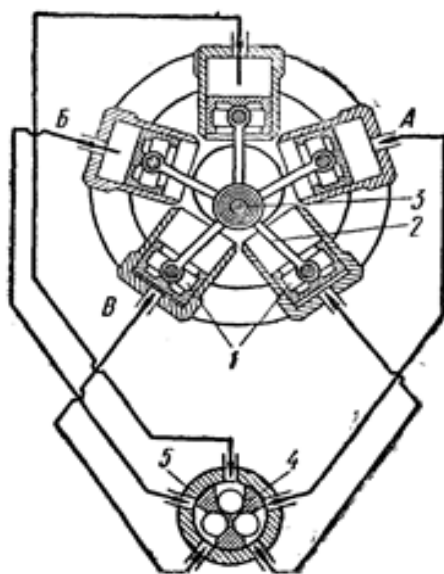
Пятицилиндровый привод вращательного движения
